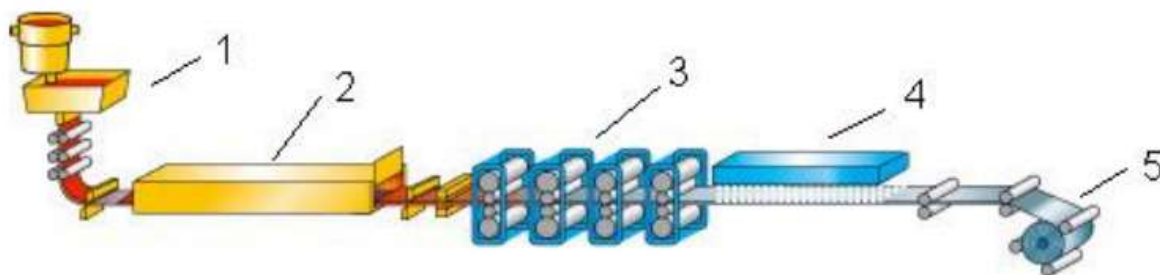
Одноручьевого агрегат CSP прямой прокатки полосы: 1- МНЛЗ; 2-проходная печь; 3-прокатный стан; 4-участок охлаждения; 5-моталка
